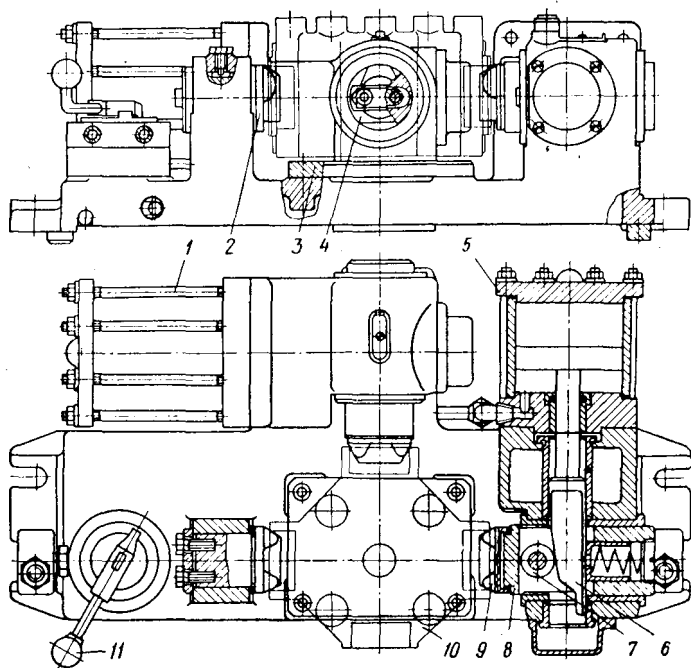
Приспособление с установкой заготовки по литым отверстиям при фрезеровании опорной плоскости
